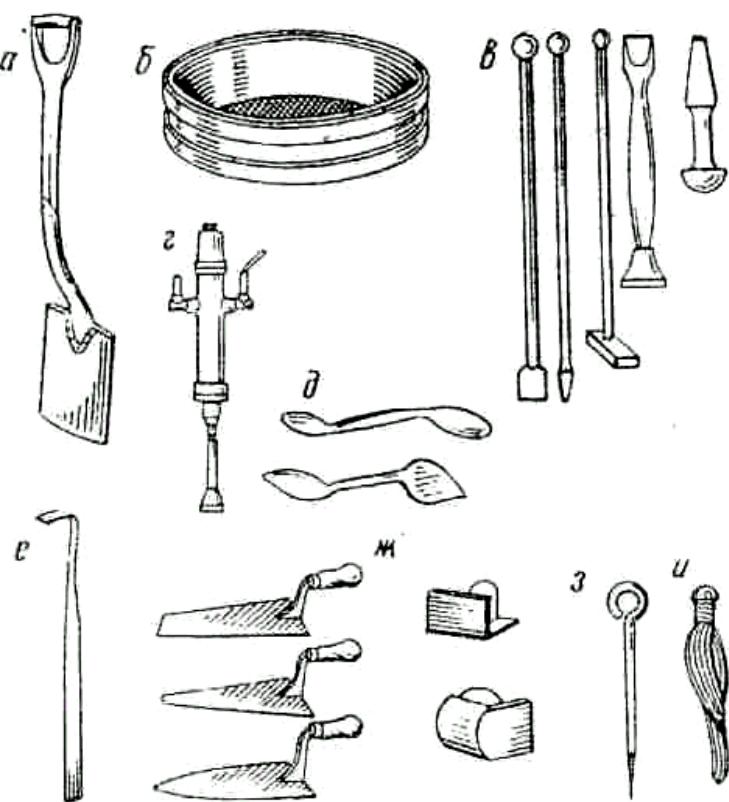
1 – Инструмент, применяемый при ручной формовке: а - ;
